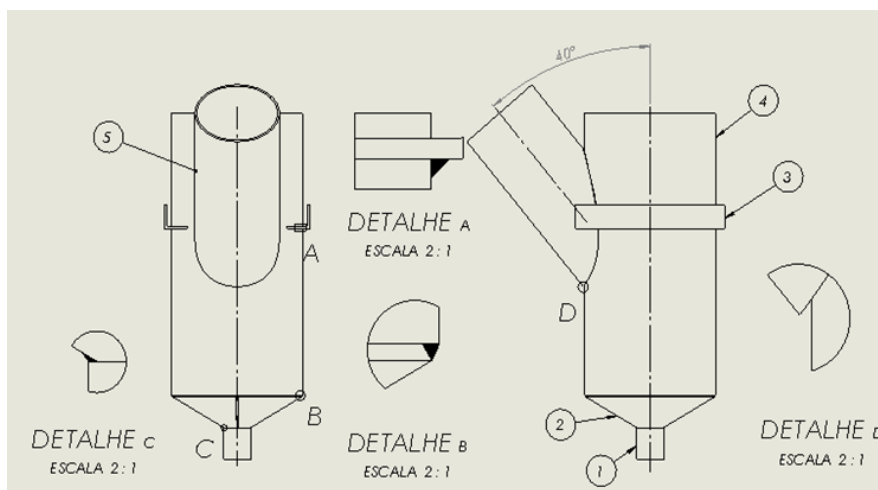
Detalhes de vistas de elementos soldados
